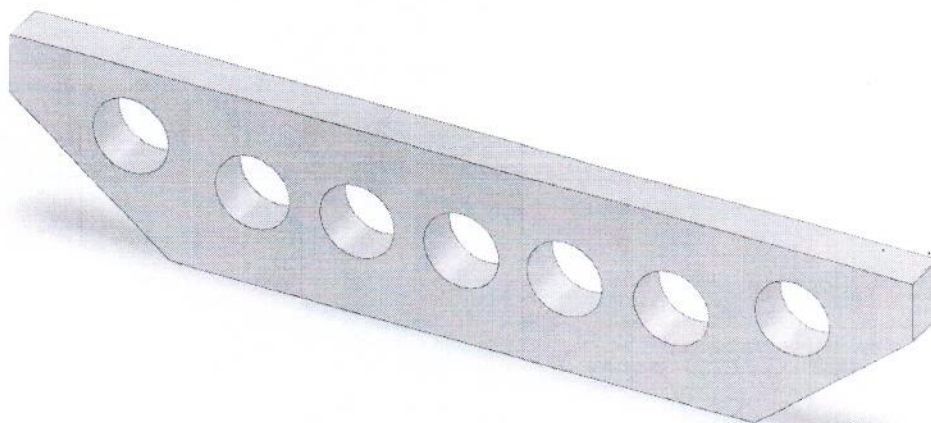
Линейка поверочная типа ШМ-ТК. Внешний вид.
